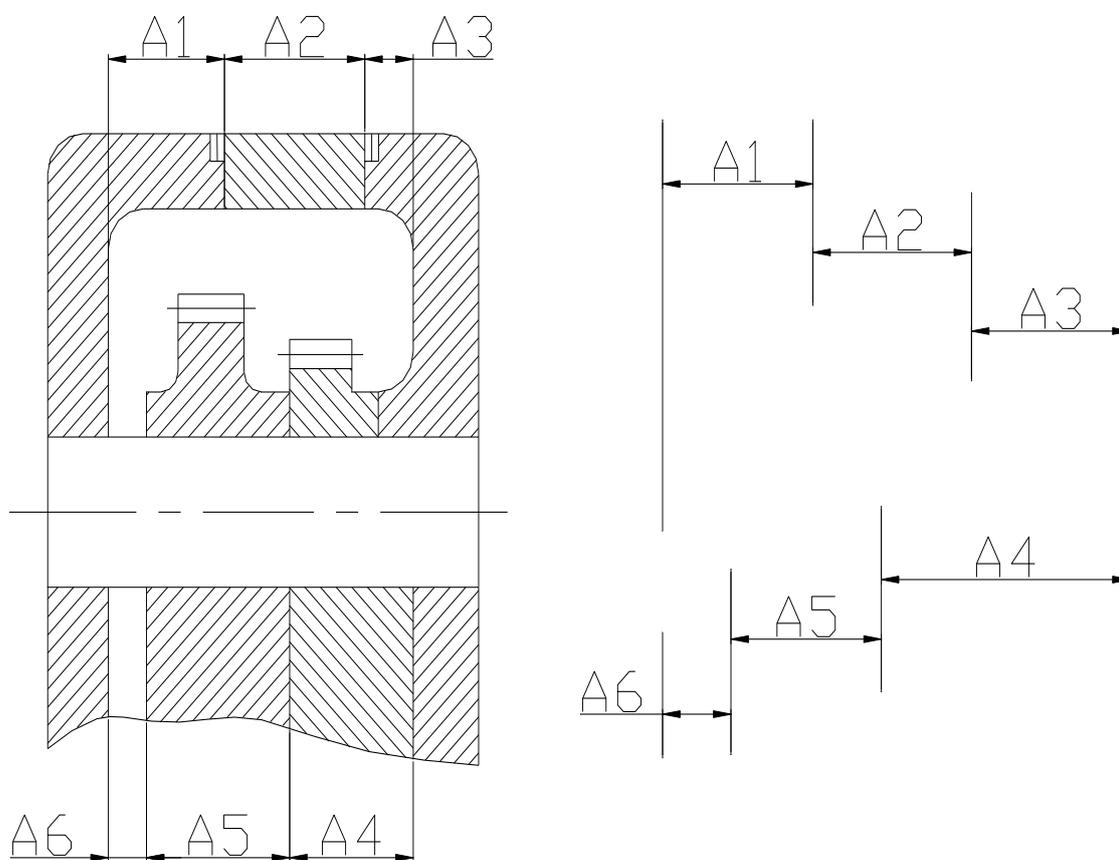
Конструктивная схема узла редуктора с указанием плоской размерной цепи
